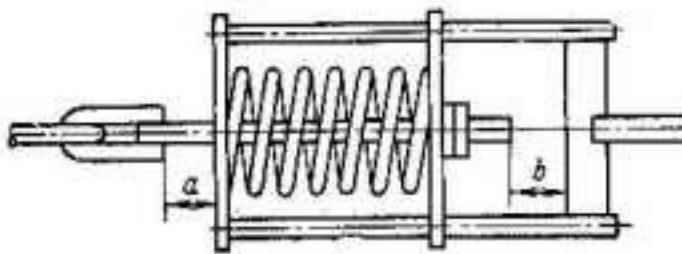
Положение пружины в металлической конструкции подвески.
